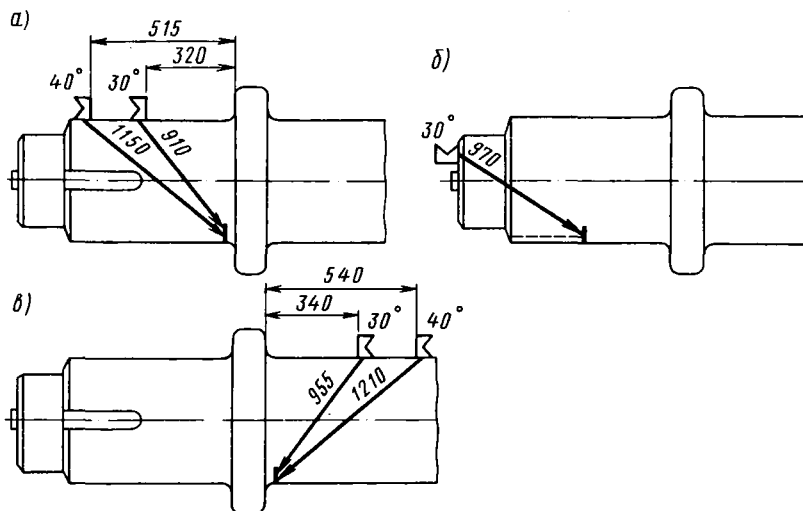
Схемы и зоны контроля главного приводного вала эскалатора Н-40М наклонными искателями со стороны правого торца
